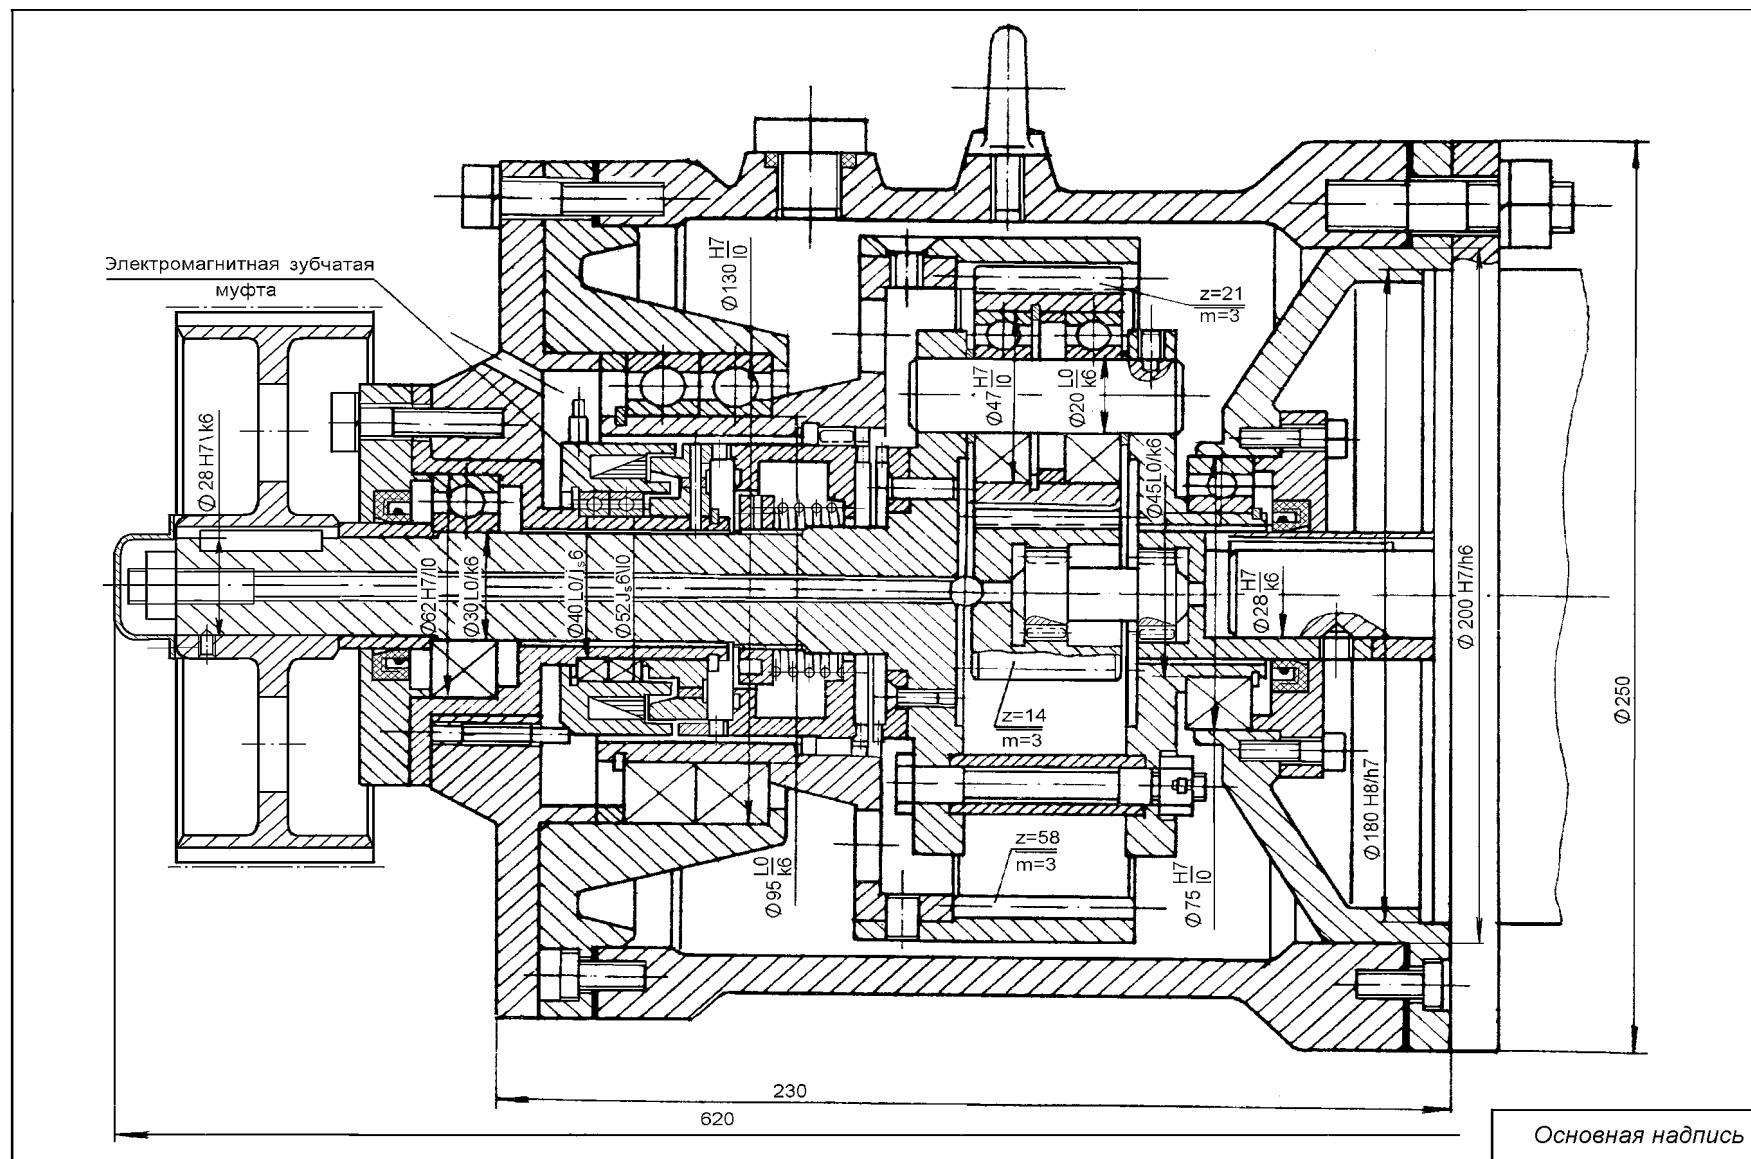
Двухскоростной планетарный редуктор (развертка)
